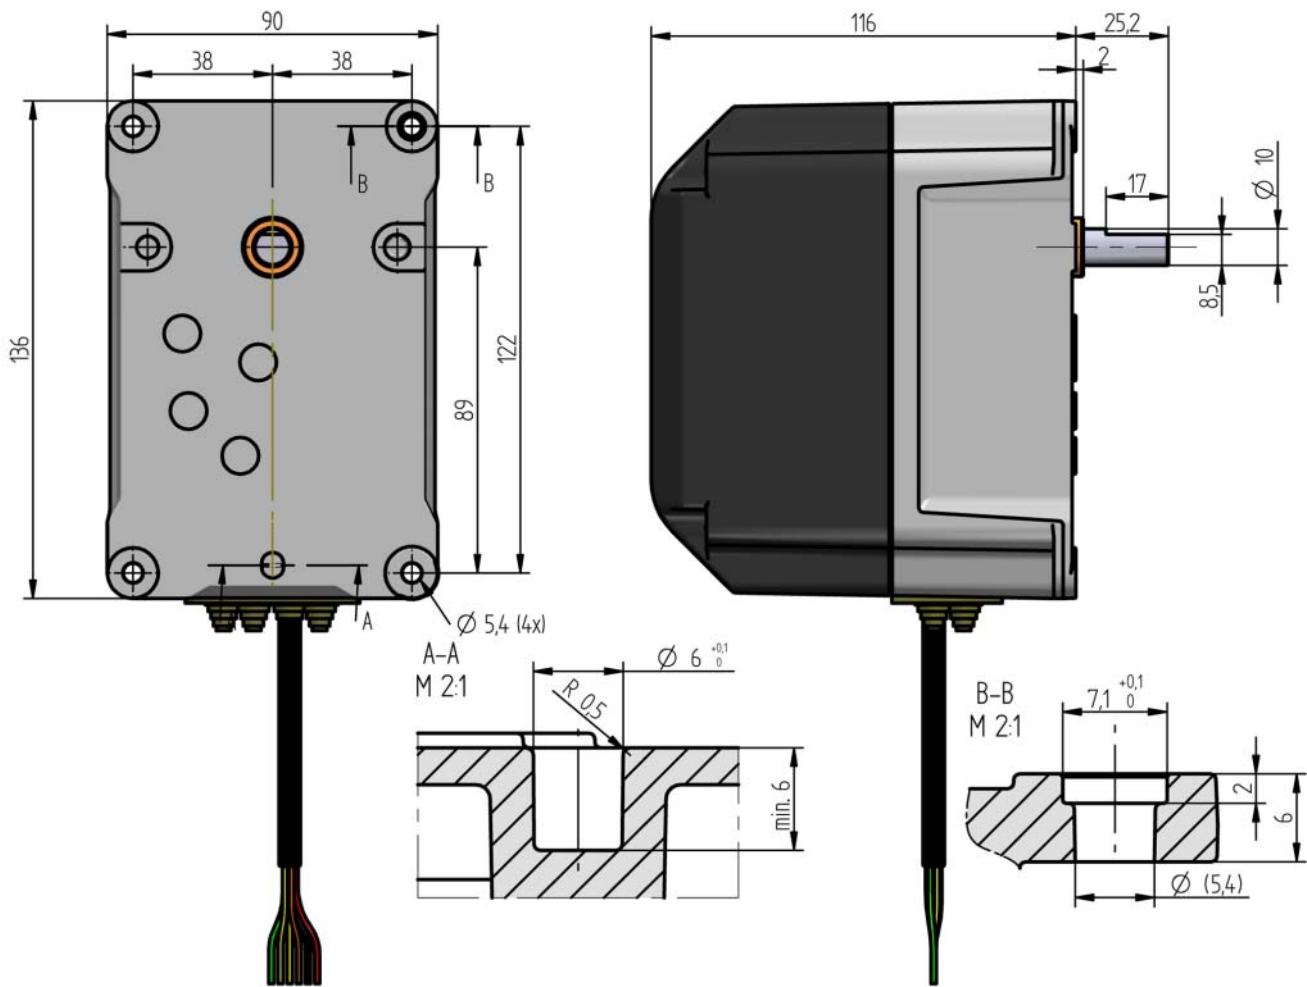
Maßbild Motor Typ 660R5001-1 und Typ 662R5003-1 mit Kabel
